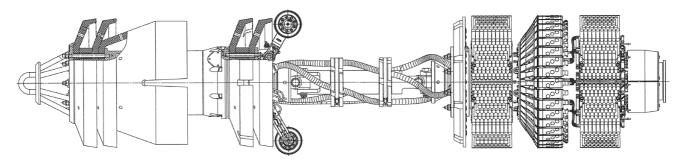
Чертеж общего вида дефектоскопа внутритрубного магнитного 16-MCK.00-00.000-00 и 20-MCK.01-00.000-01
